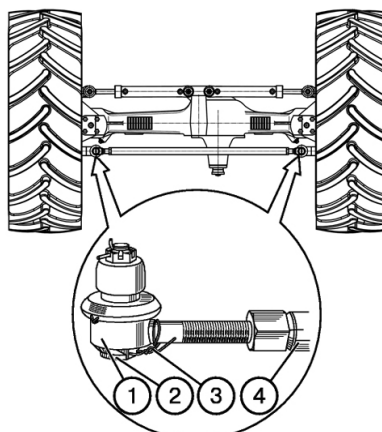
Проверка люфта рулевого колеса
